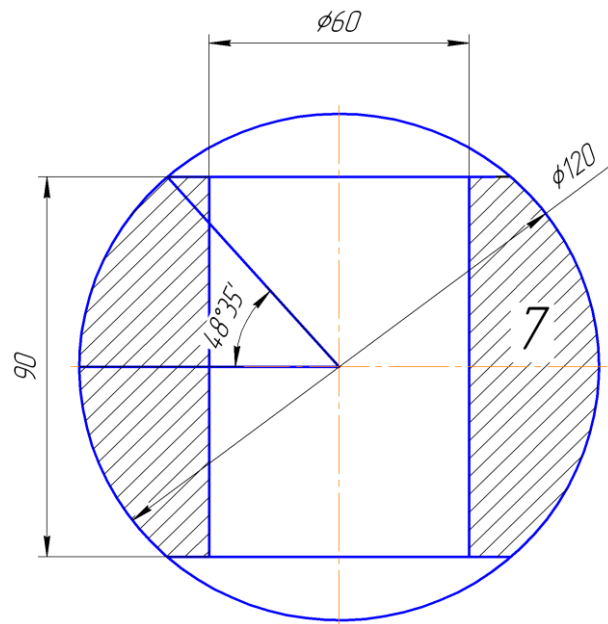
Площа поперечного перетину вала на 6-й ділянці
